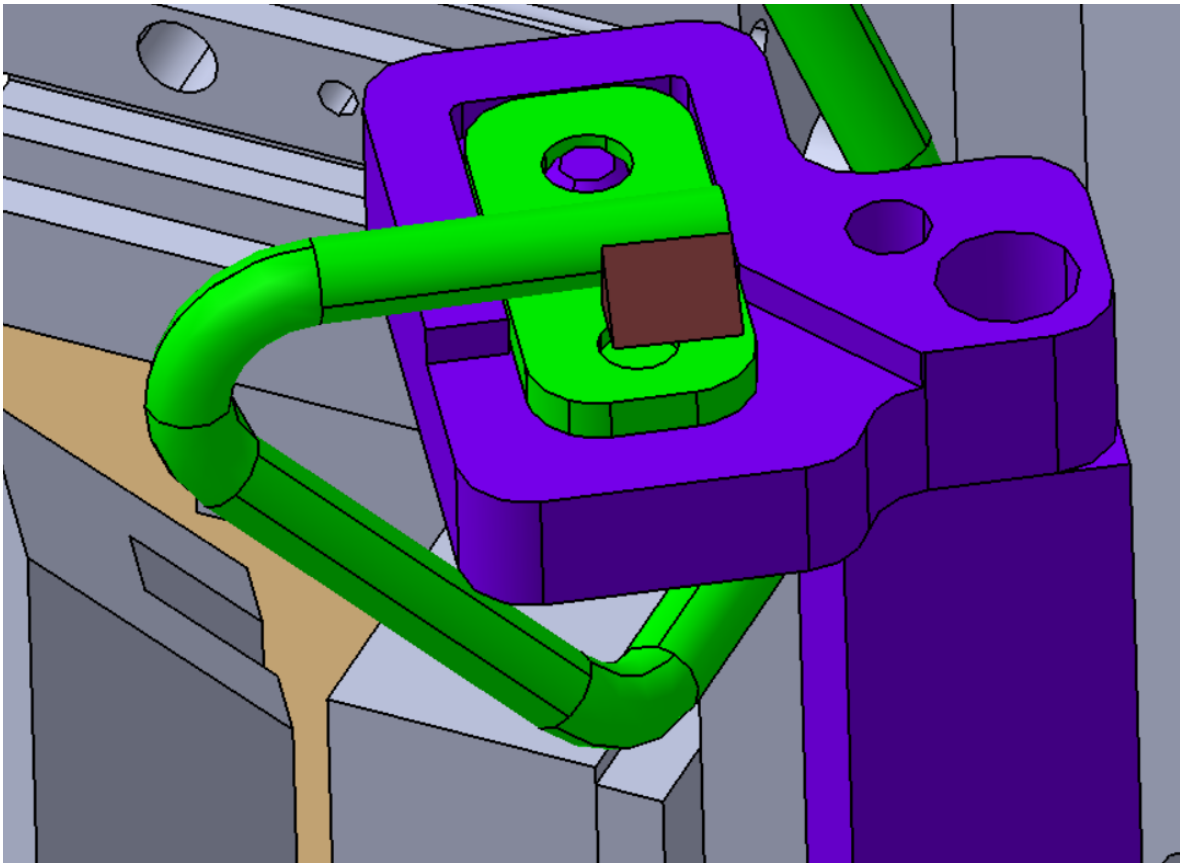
CAMBIO DE INGENIERÍA CONSIDERANCÓN DE SOLDADURA
